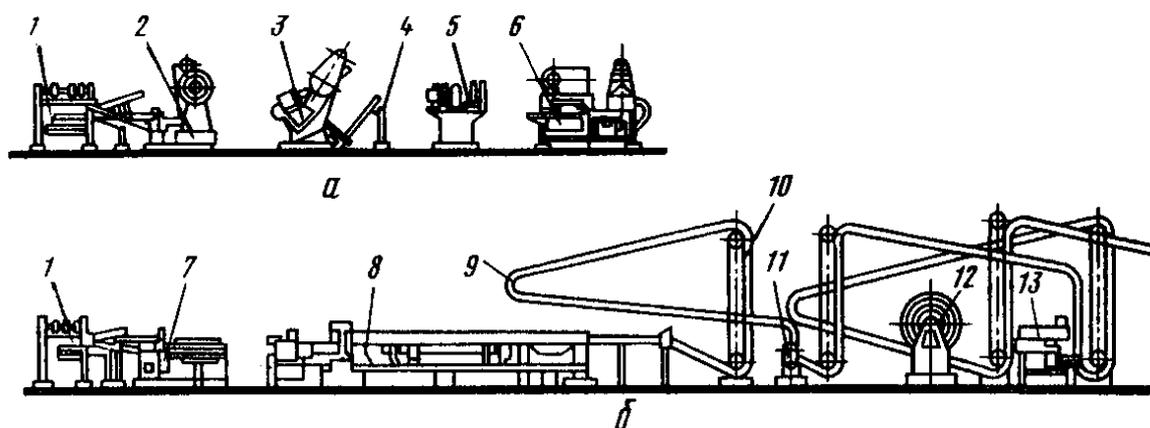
Технологическая схема изготовления сборных жестяных банок: а -концевое отделение; б - корпусное отделение; 1 - устройство для подачи жести; 2 - однорядные фигурные ножницы; 3 - однорядный пресс; 4 -
